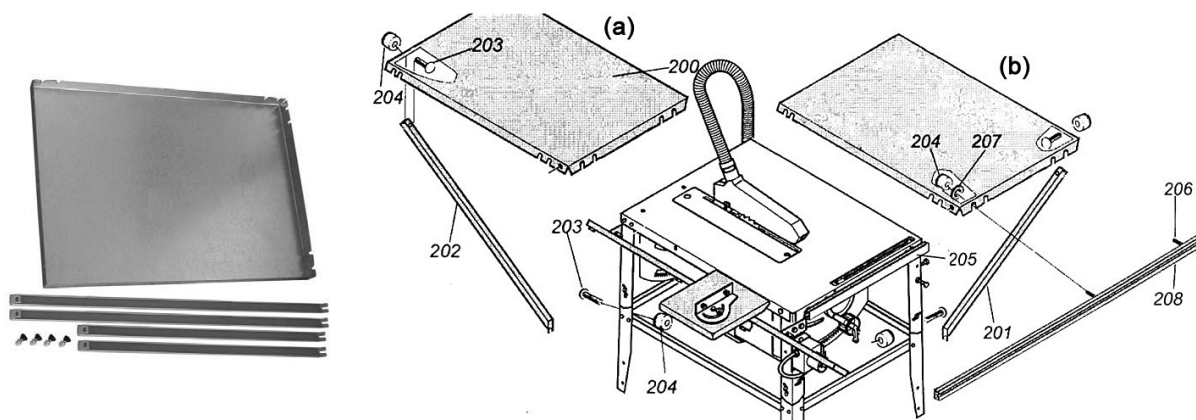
Extensão de mesa: componentes e montagem traseira (a) e lateral direita (b)
